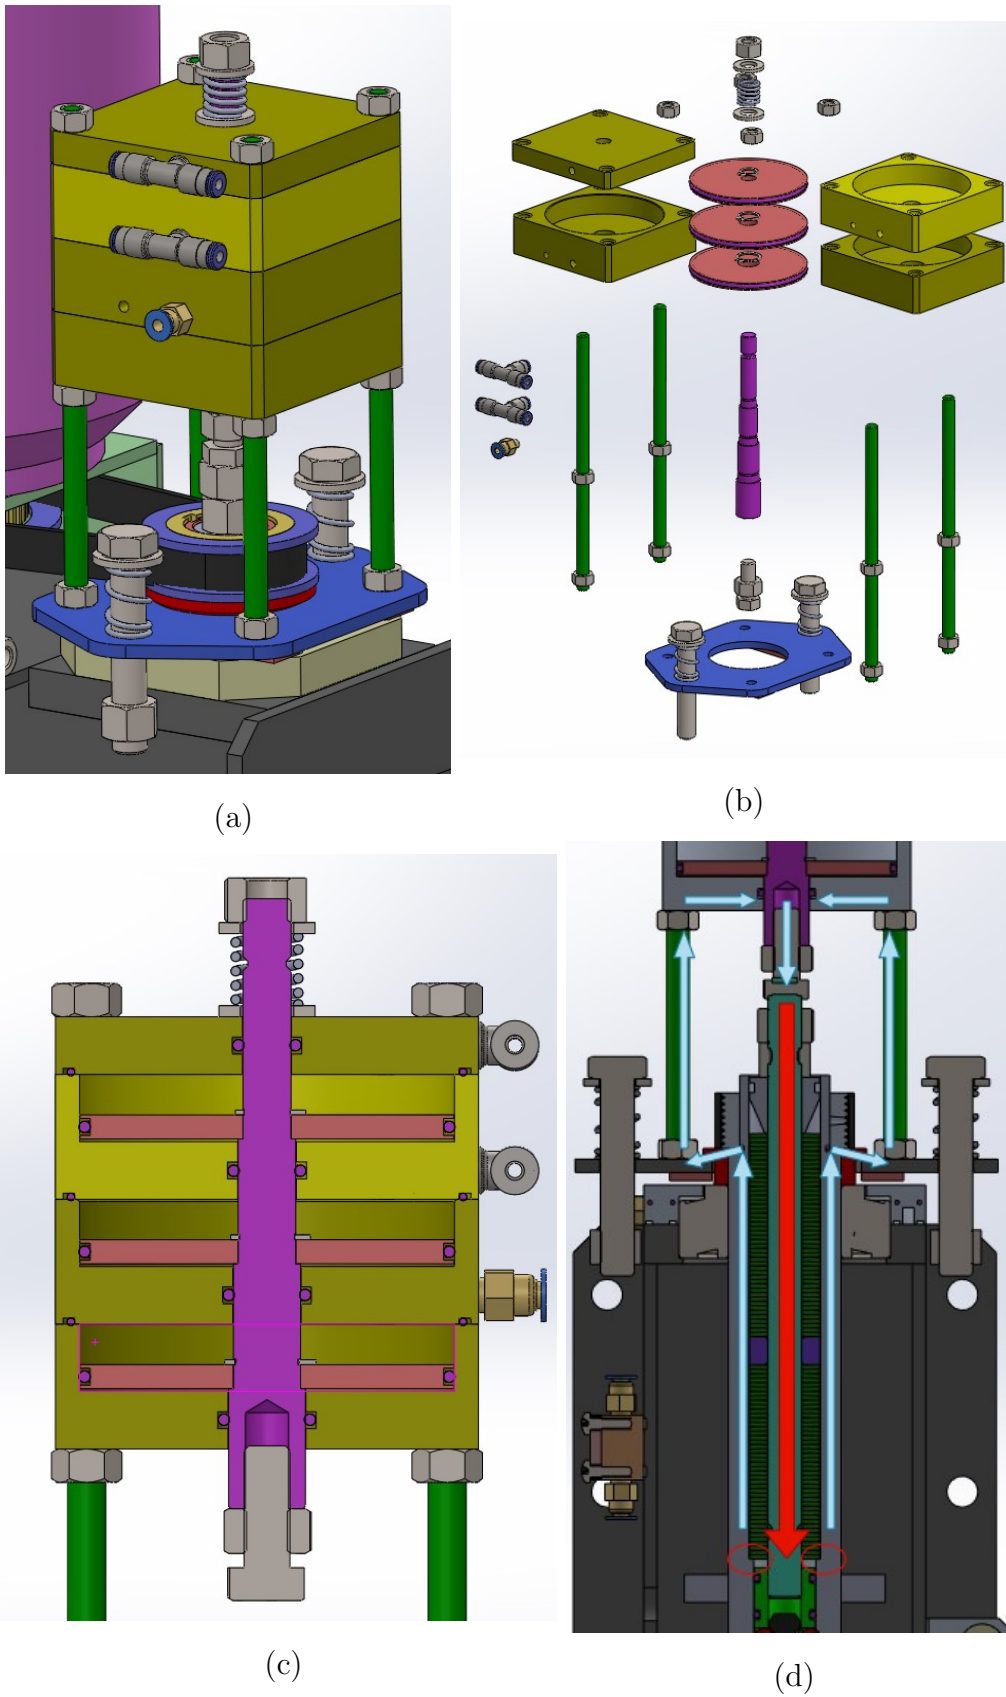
Vista isométrica(a); Vista explosionada (b); Sección transversal (c); Recorrido fuerzas (d).
